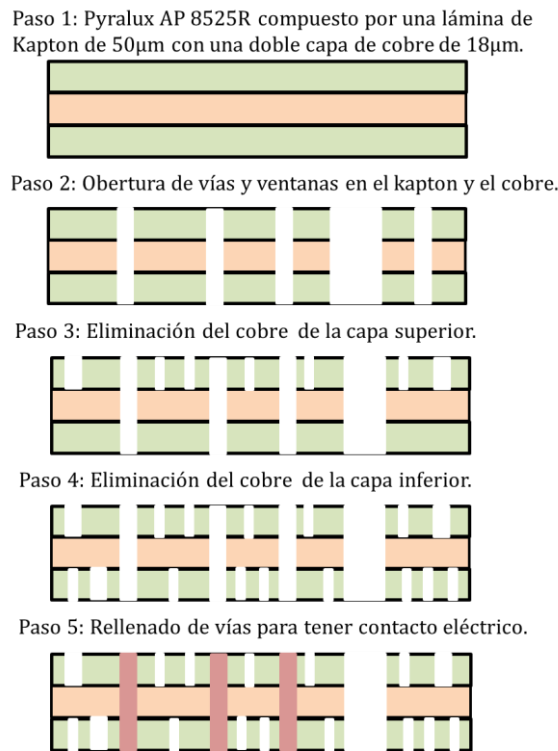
Proceso de fabricación del PCB de la tarjeta RFID en formato flexible.
